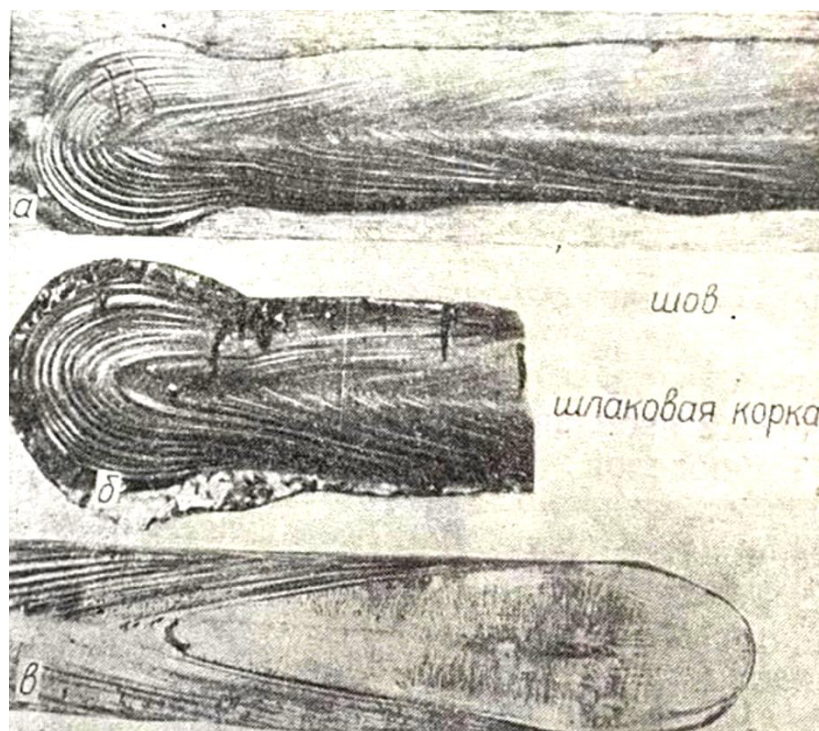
Вид шва, сваренного под флюсом: а – поверхность шва; б – шлаковая корка, удаленная со шва; в – конечная часть шва [1]
